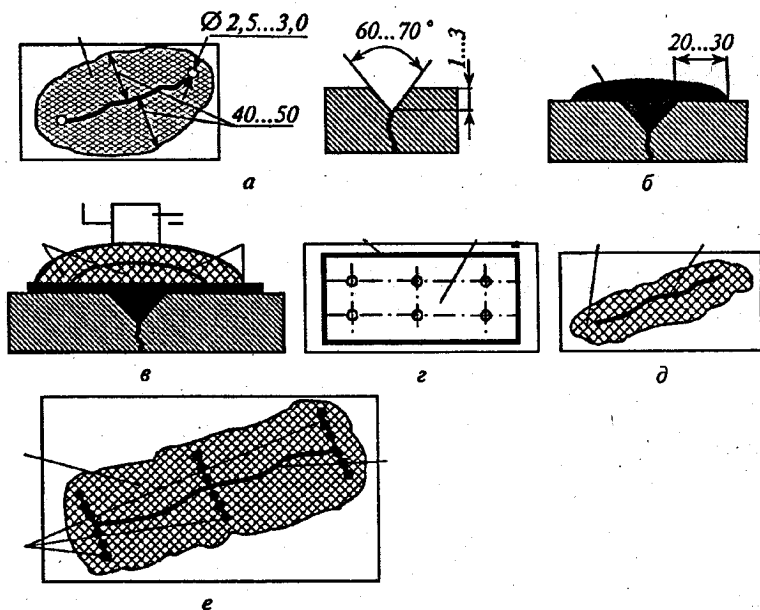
Применение полимерных материалов при заделке трещин (*а–г, е*) и пробоин (*д*): 1 — зона подготовки поверхности; 2 — композиция; 3 — стеклоткань; 4 — ролик; 5 — стальная накладка; 6 — сварочный шов; 7 — фигурная вставка; 8 — трещина
